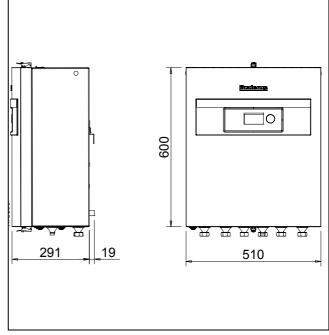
Dimensioni di ingombro Modulo idraulico interno AW in mm
